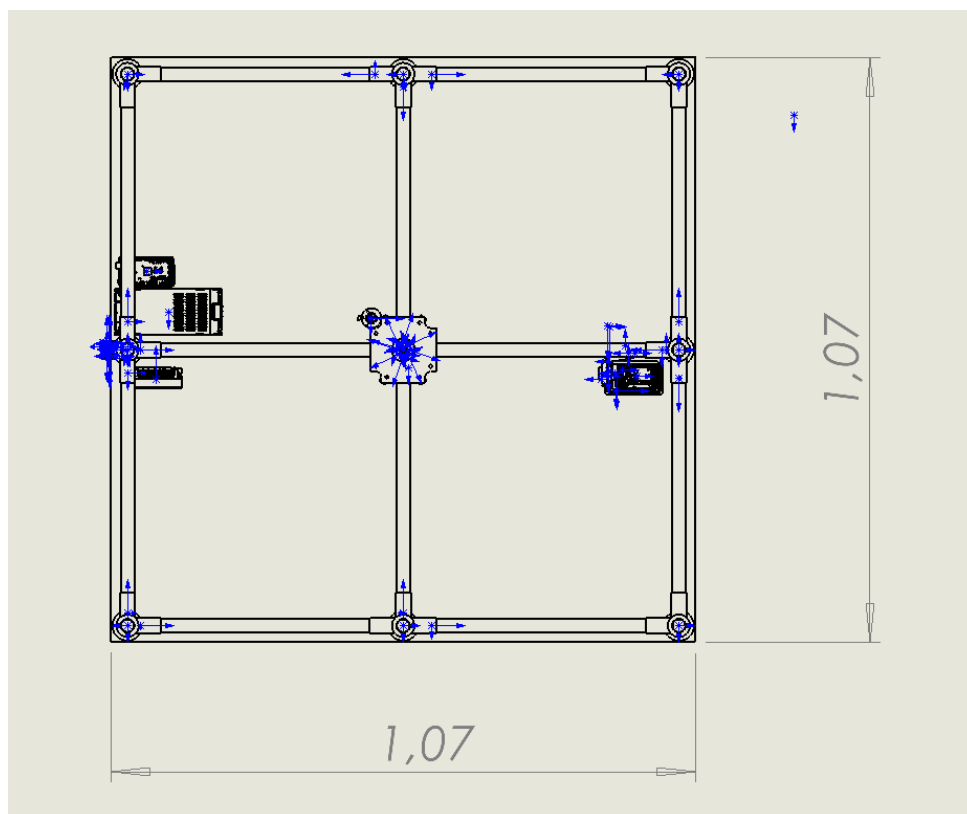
Креслення вид зверху (розмір в метрах)
